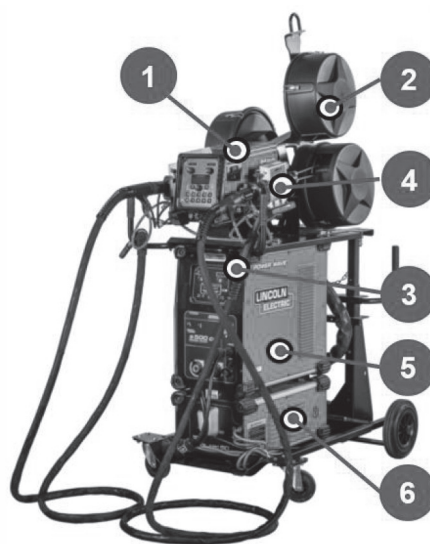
Instalație de sudare: 1) Derulator; 2) Suport role; 3) Pistol de sudare; 4) Sistem alimentare sârmă 5) Sursa de sudare; 6) Sistem de răcire
